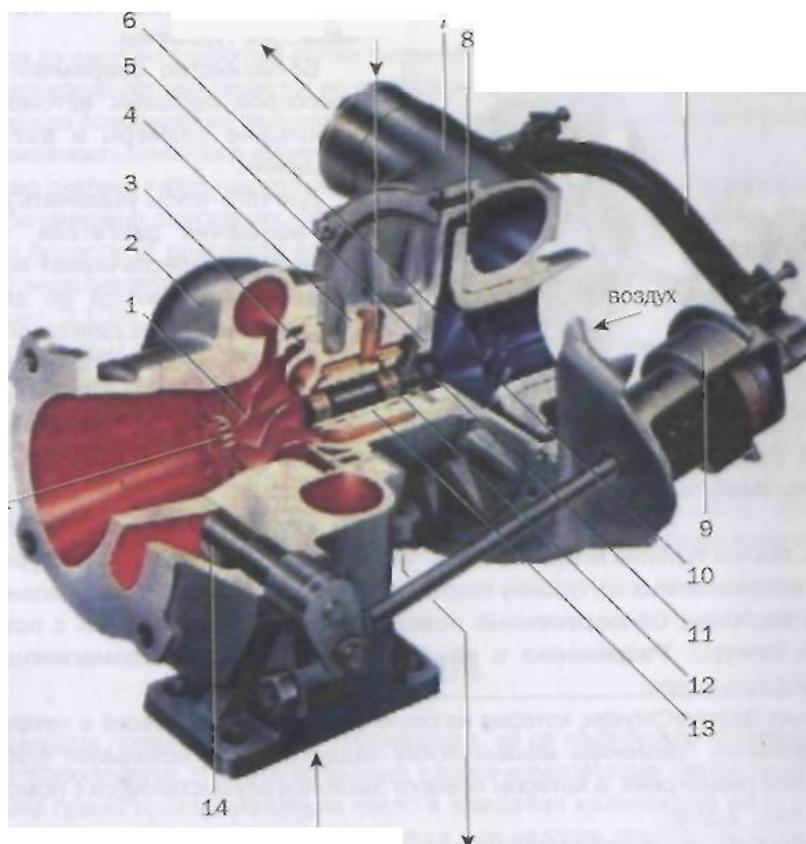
Турбокомпрессор Garrett: 1 - лопатки турбины; 2 - корпус турбины; 3 - тепловая защита; 4 - корпус подшипников; 5 - упор; 6 - защитная пластина; 7 - корпус компрессора; 8 - диффузор; 9 - клапан; 10 - насос компрессора; 11 - уплотнение; 12 - подшипник; 13 - втулка подшипника; 14 - заслонка
